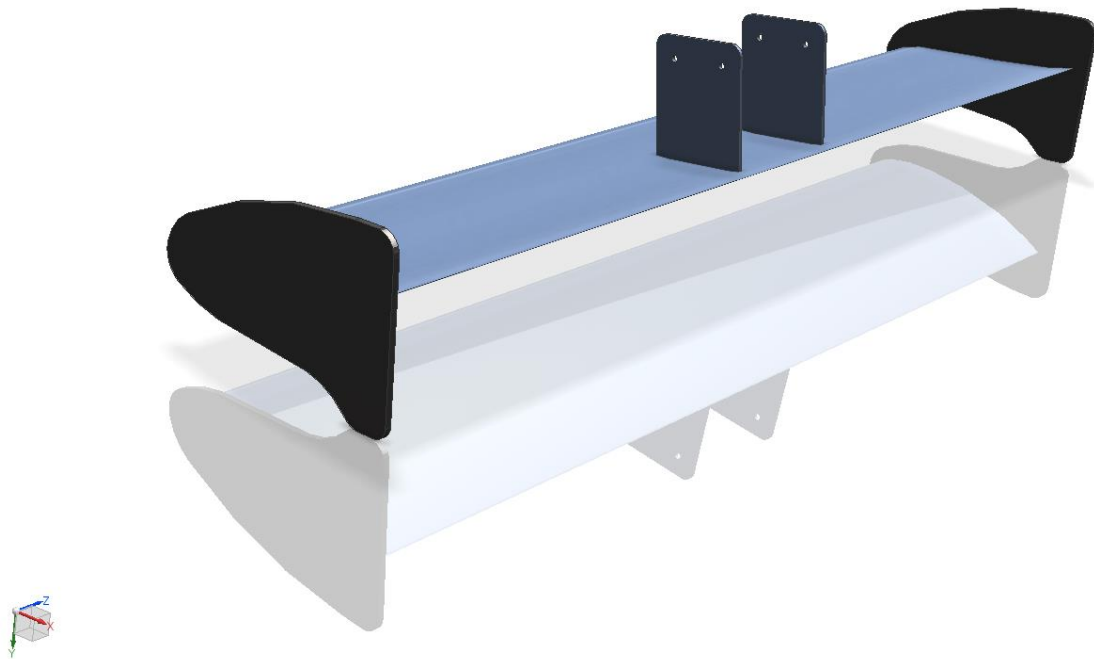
Vista posterior de l'assemblatge de l'aleró davanter. [Autor]
